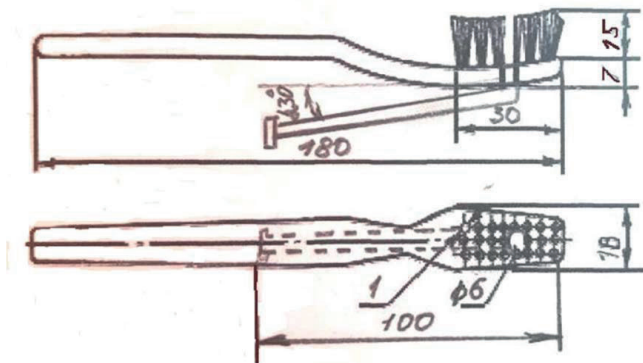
Чертеж прибора «Зубная щетка с насадкой для ирригатора».
